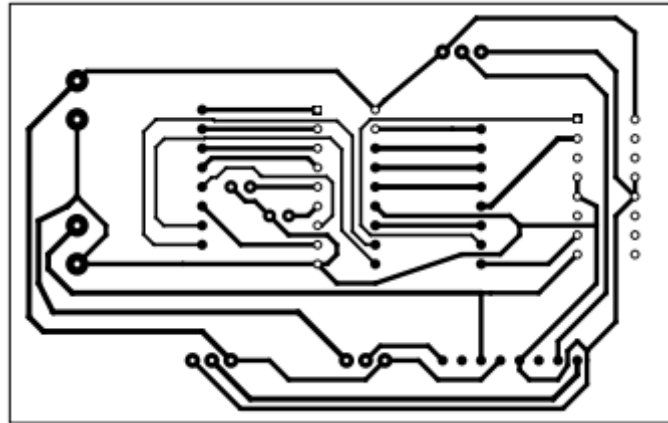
Diseño de las pistas del motor DC para la placa PCB.
